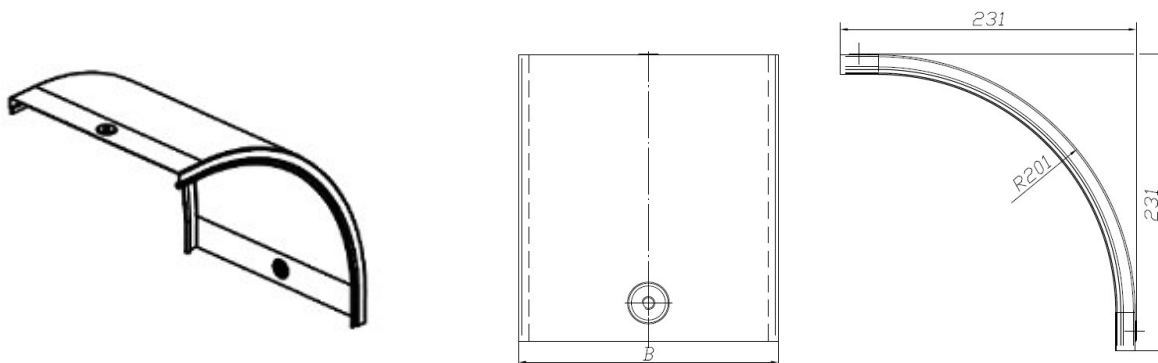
Крышка CD 90 на угол вертикальный внешний 90°
